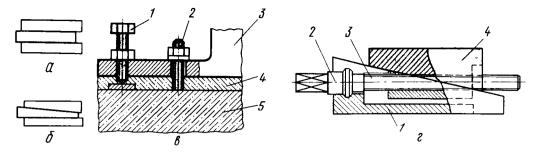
Приспособления для выверки и регулировки положения оборудования:
